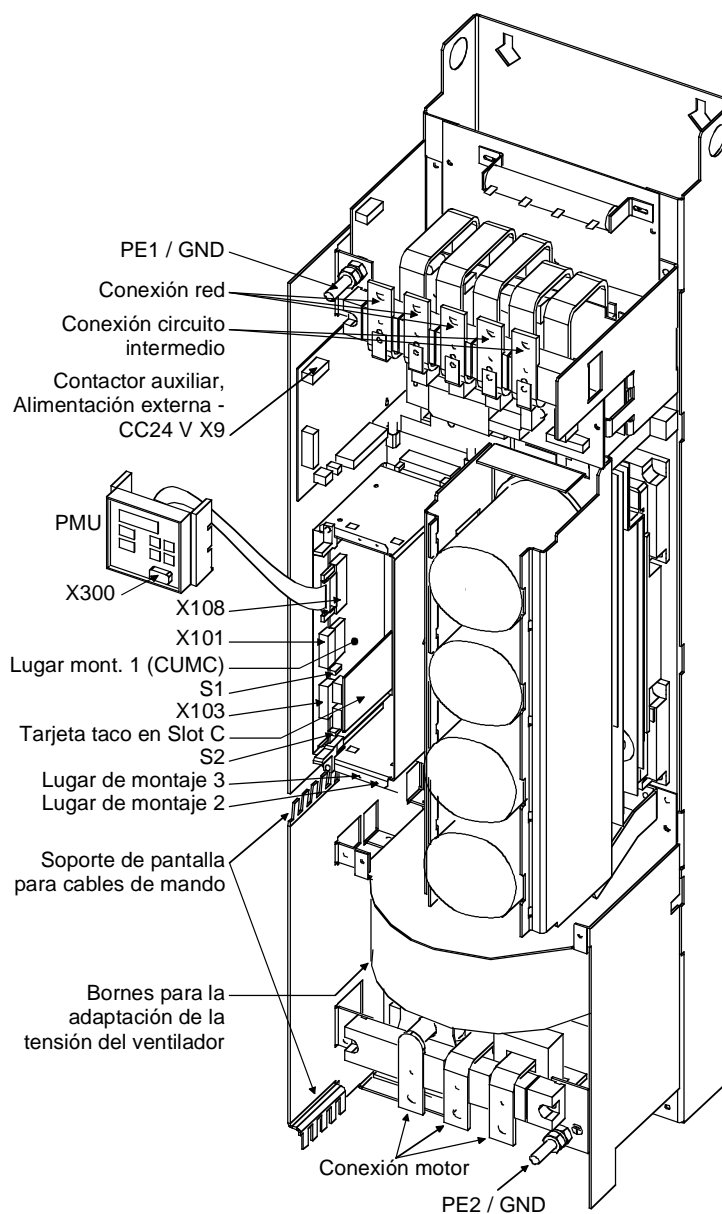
Esquema de conexiones, forma constructiva E y F
